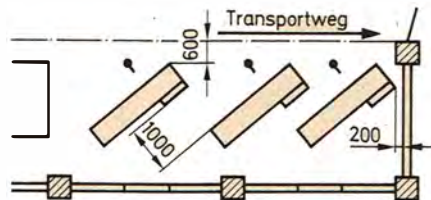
Umrißzeichnung, Aufstellen von Drehmaschinen
